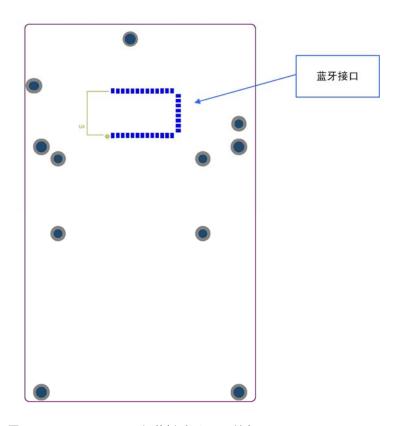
MTP58-FTxx-T1 评估板反面 PCB 丝印
